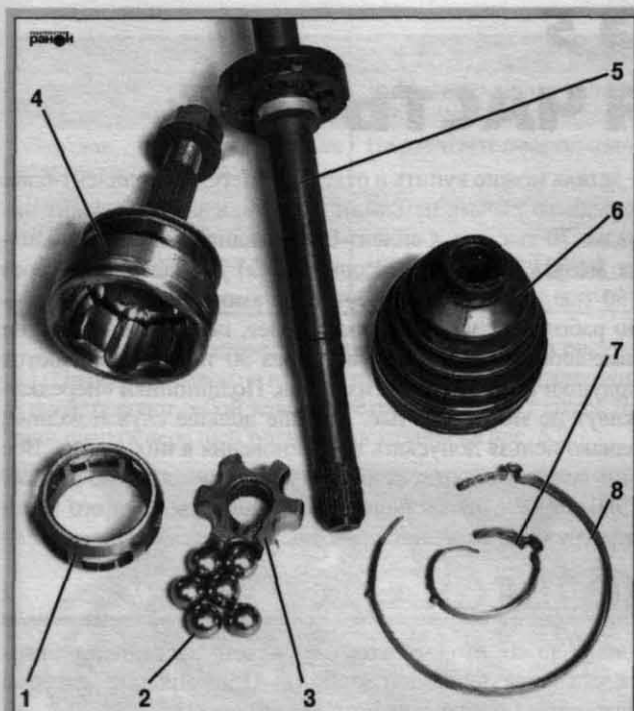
Детали ШРУСа («гранаты»): 1 – сепаратор; 2 – шарик; 3 – обойма; 4 – корпус ШРУСа («гранаты»); 5 – полуось с гасителем крутильных колебаний; 6 – пыльник; 7 – короткий хомут; 8 – длинный хомут
